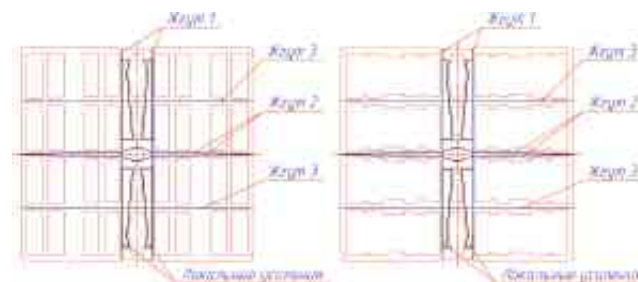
Общий вид жгутов и локальных усилений в конструкции оболочек:
